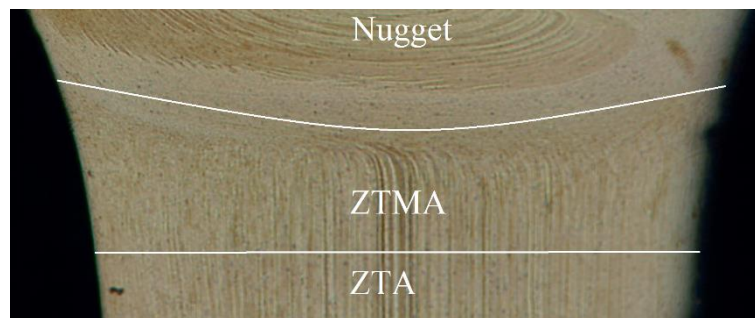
Diferentes zonas do *nugget/stringer* da soldadura 562BRP-1.(Imagem ampliada da Figura 4.4)
